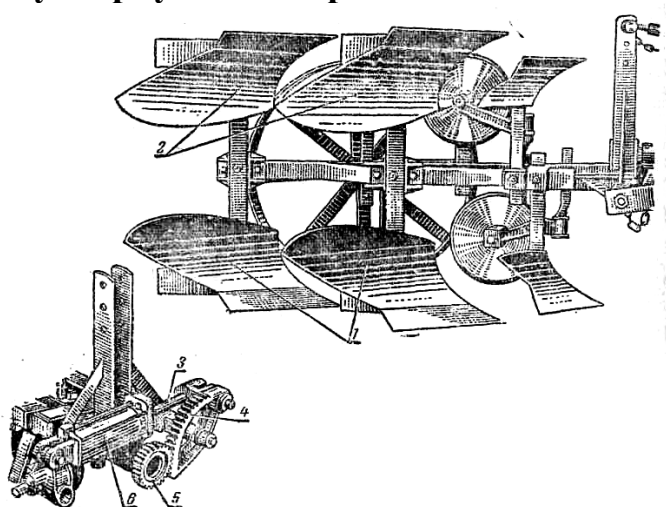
Навесной оборотный двухкорпусный плуг ПОН-2-30:
